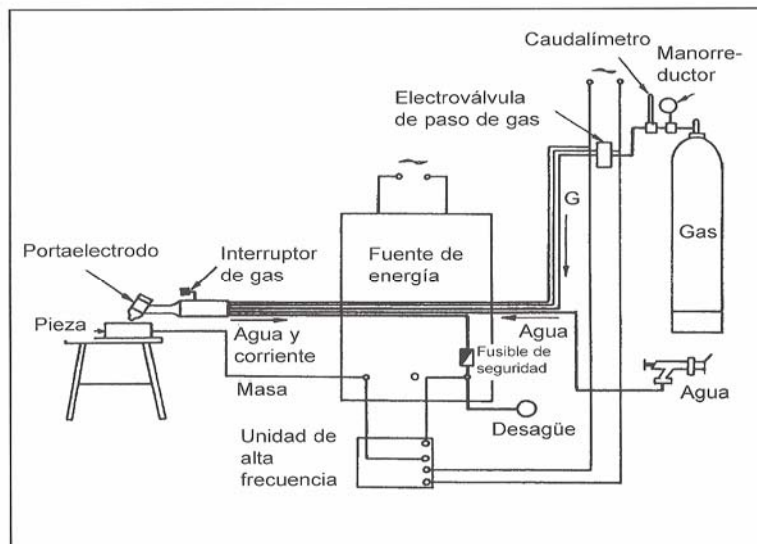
Esquema de una instalación para soldadura TIG.
